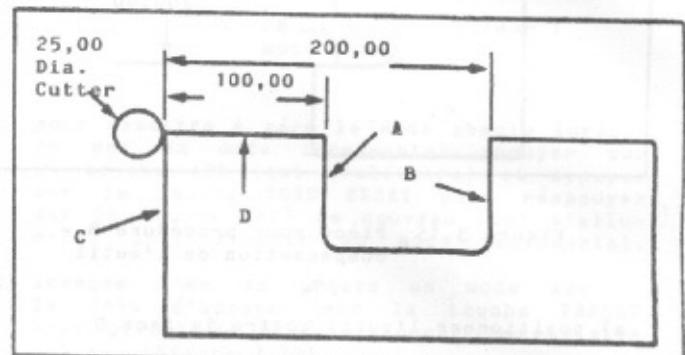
Pièce pour procédure A - compensation de l'outil
